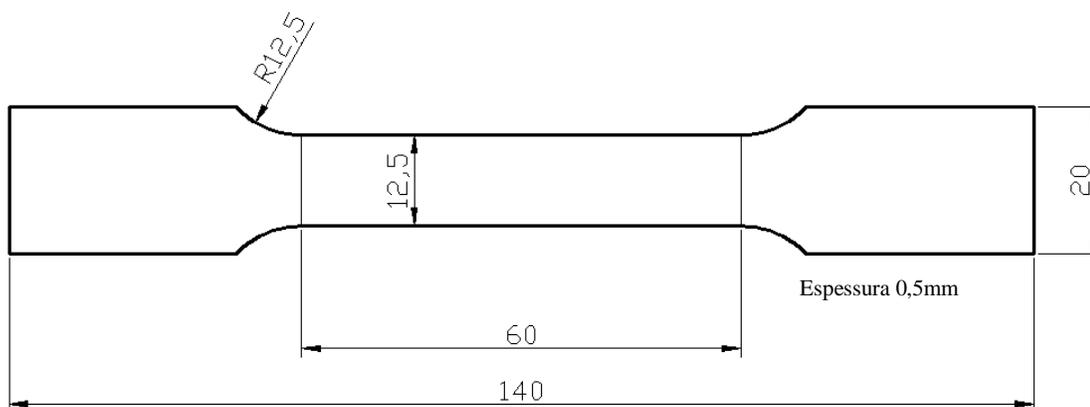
Corpo de prova com as dimensões padronizadas.
